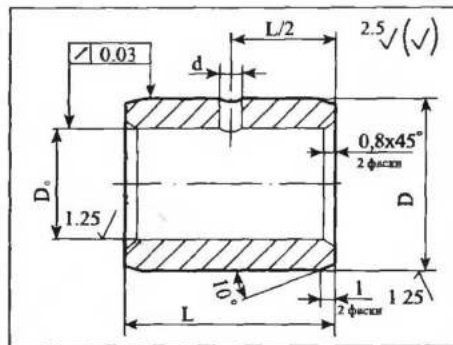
Эскиз бронзовой втулки верхней головки шатуна:
